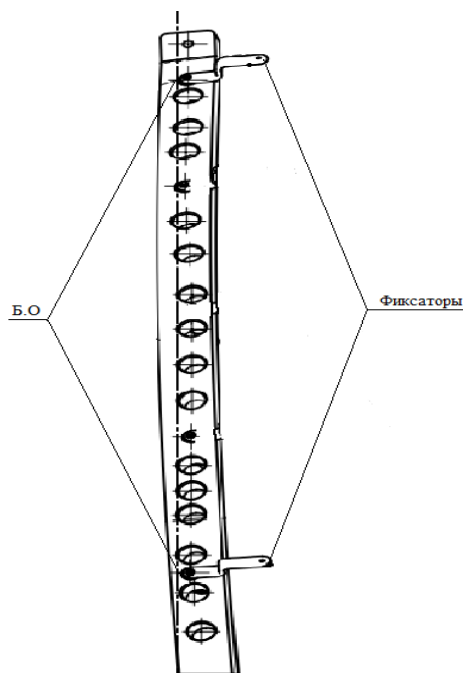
Кондукторов для сверления отверстий по соединению шпангоутов с обшивками
